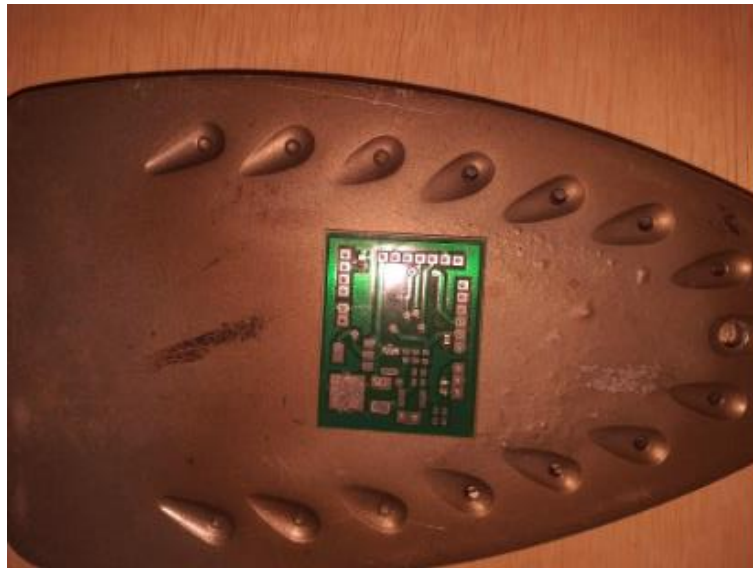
Placa PCB sobre el Equipo de soldadura
